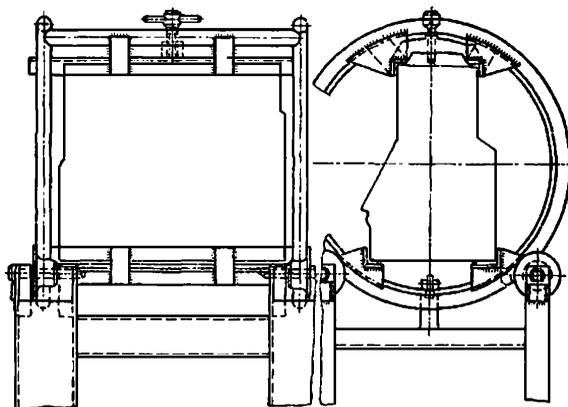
Приспособление для повертывания собираемого автомобильного двигателя
